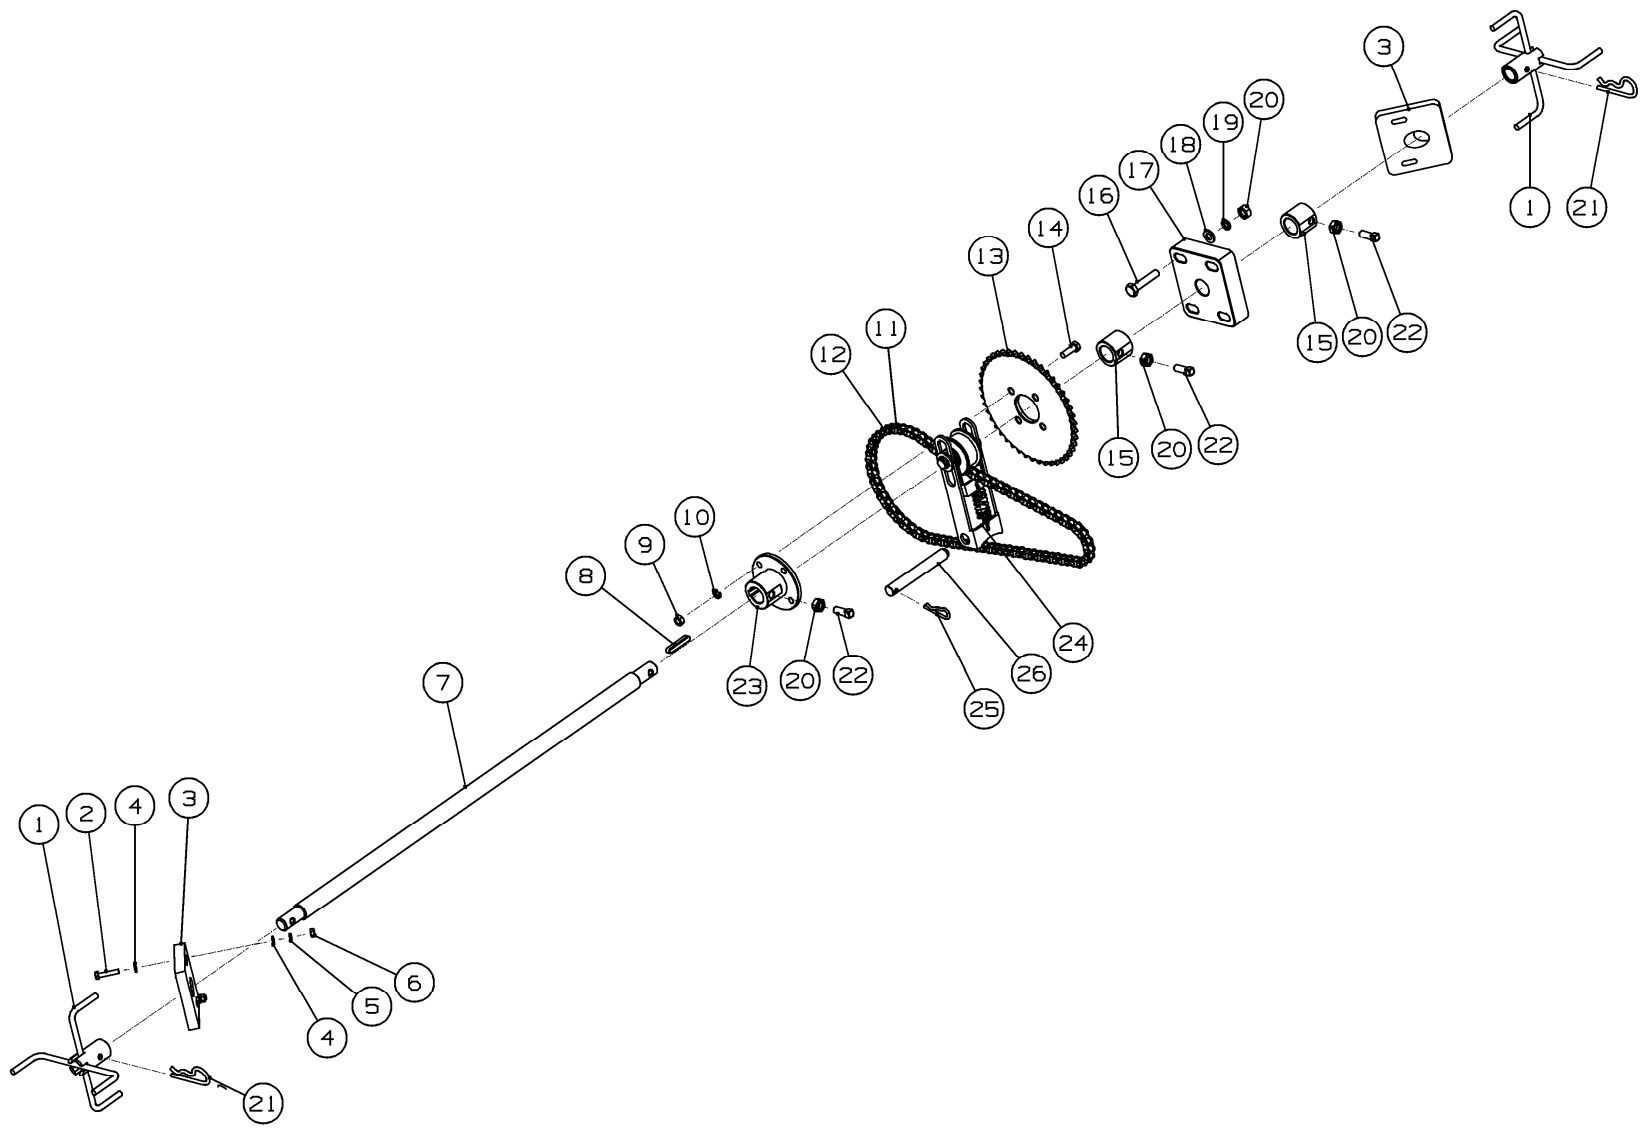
Установка ворошилки РА-900.90.00.000Б
